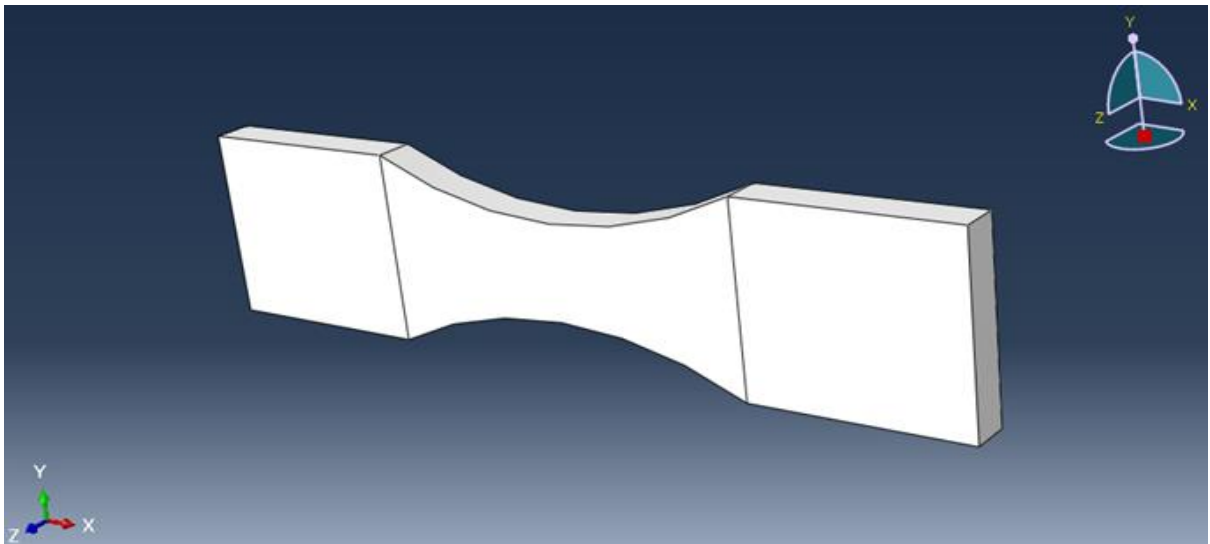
modèle géométrique de l'éprouvette non soudée
